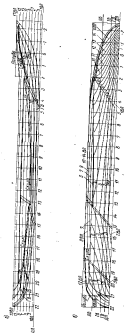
Теоретический чертеж корпуса теплохода «Вихрь»: а — борту; б — левому борту.
